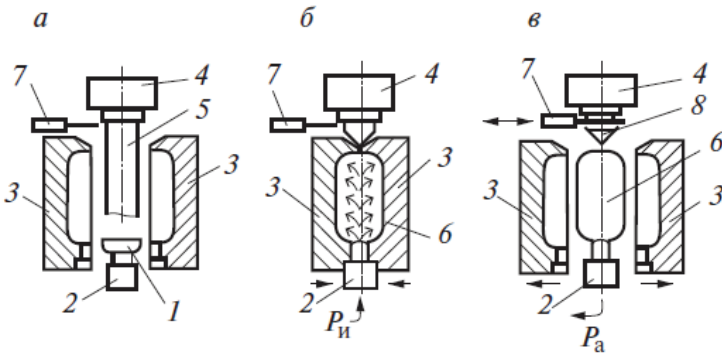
Схема інжекційно-екструзійного роздуву тари
